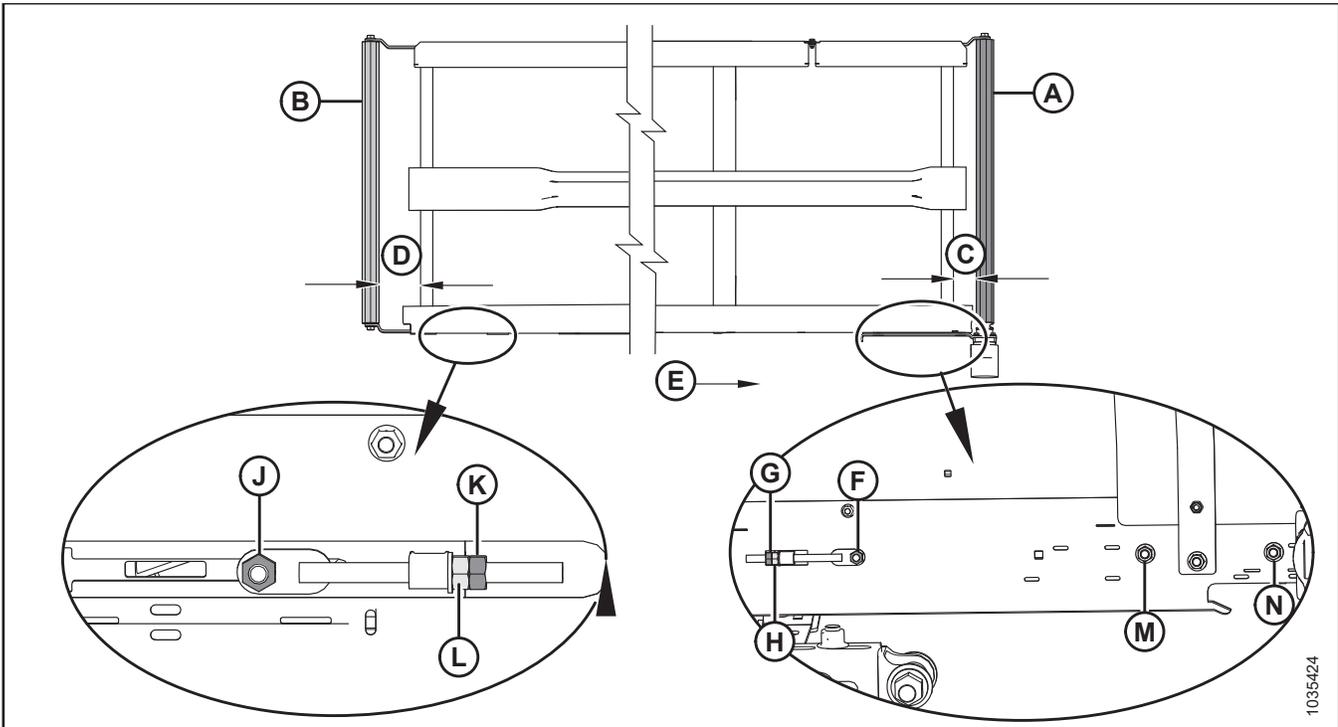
Réglage de l'alignement du tapis – Tapis gauche
